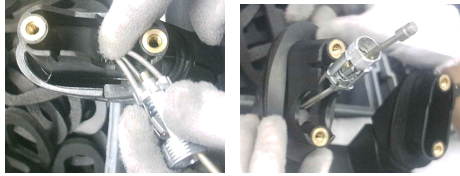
Üst kol tapası+gövde tapaları montajı
